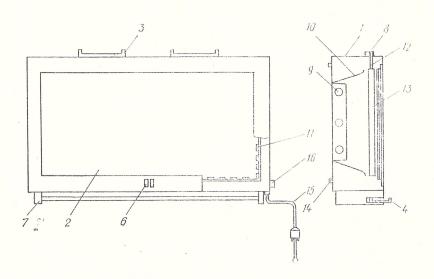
Негатоской НШ-80 I — корпус; 2 — экран; 3 — кроиштейн; 4 — лоток; 6 — выключатель; 7 — ножка; 8 — ручка управления; 9 — лампа люминисцентная; 10 — отражатель света; 11 — прижим; 12 — ось; 13 — шторка; 14 — крышка; 15 — шнур питания; 16 — предохранитель.
